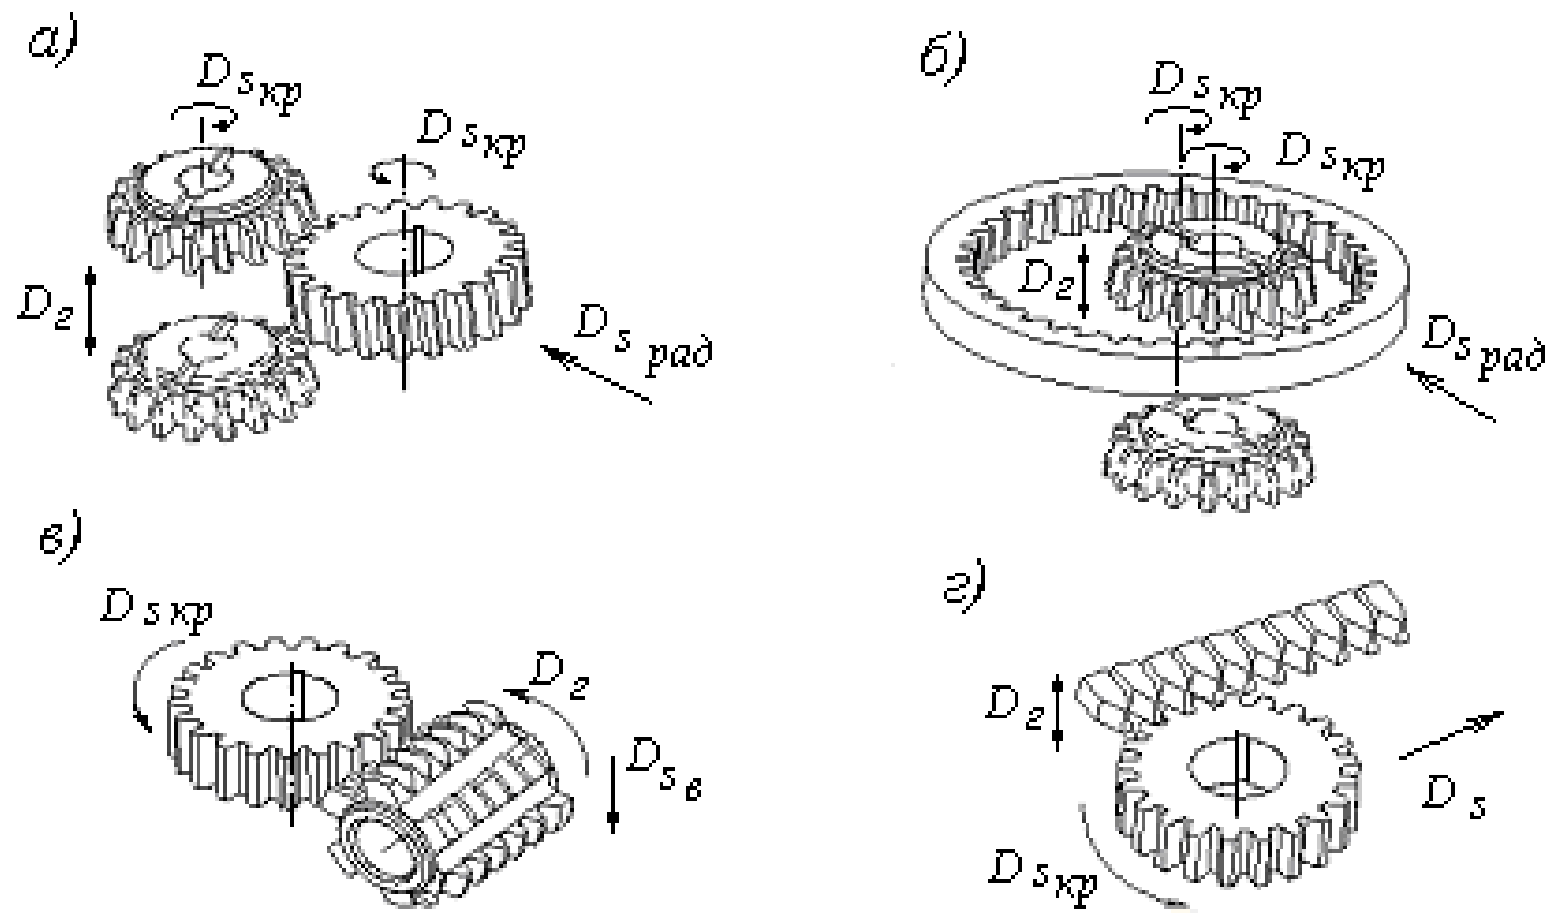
Схемы обработки венцов зубчатых колёс методом обкатки
